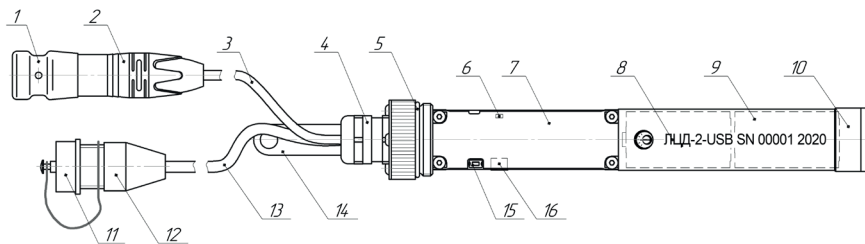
Габаритный чертеж логгера цифровых датчиков ЛЦД-2-USB
